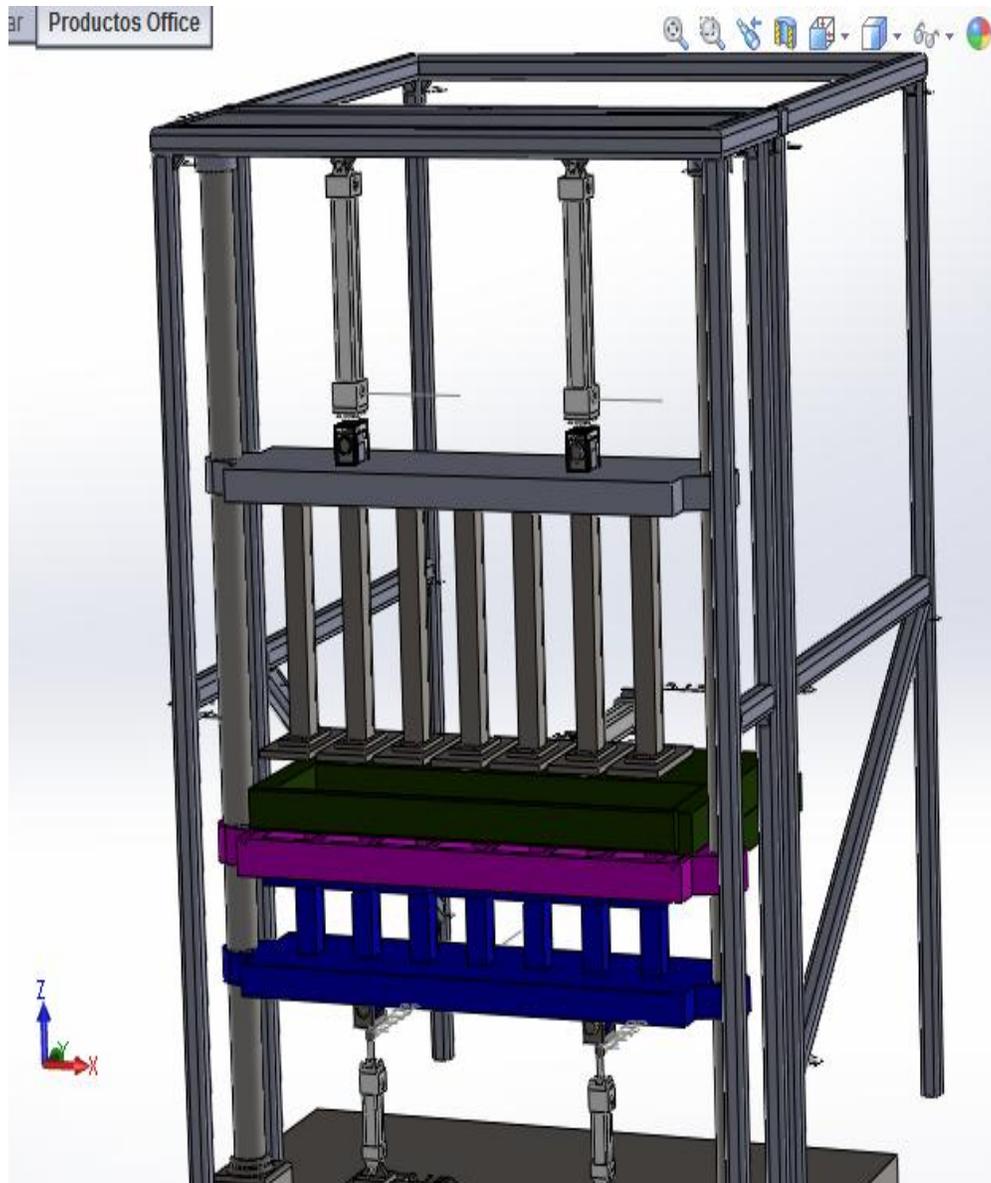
Representación del ensamble de la máquina, se visualiza el sistema de moldeo
